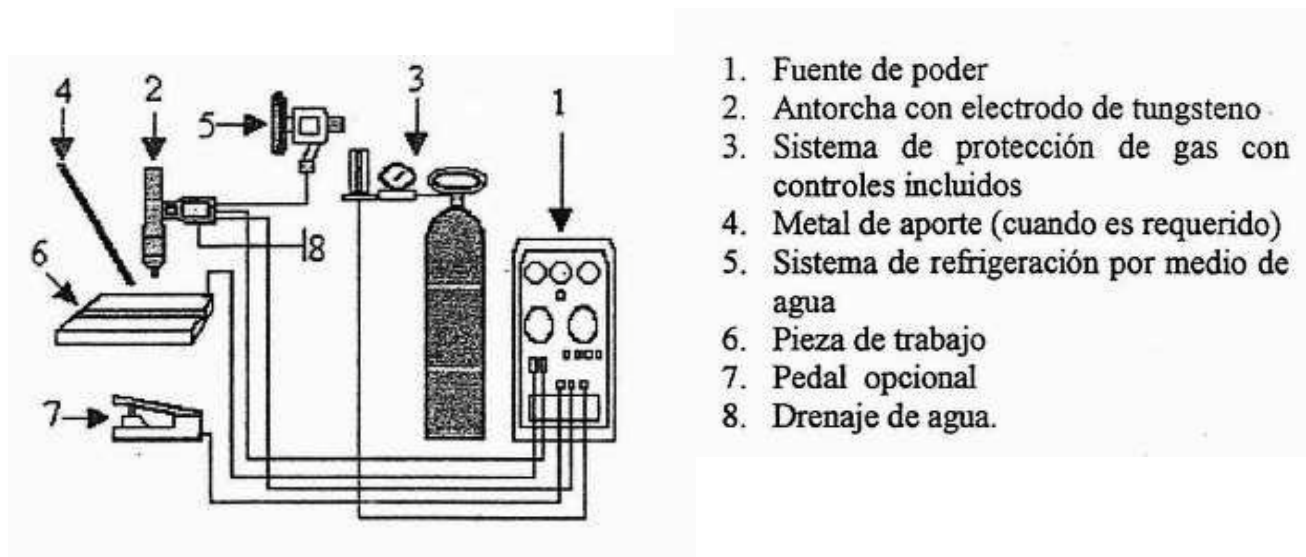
EQUIPO EMPLEADO EN EL GTAW
